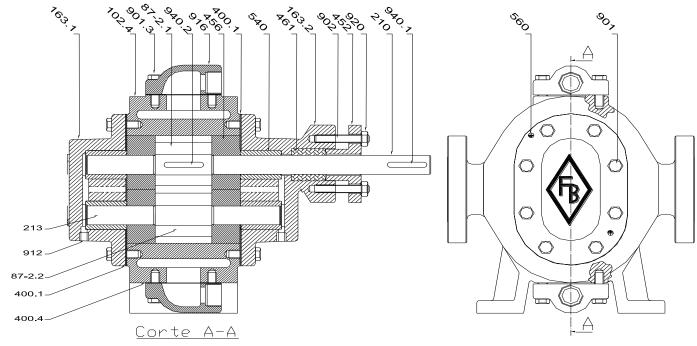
Desenho em Corte bomba FBE c/ Câmara
